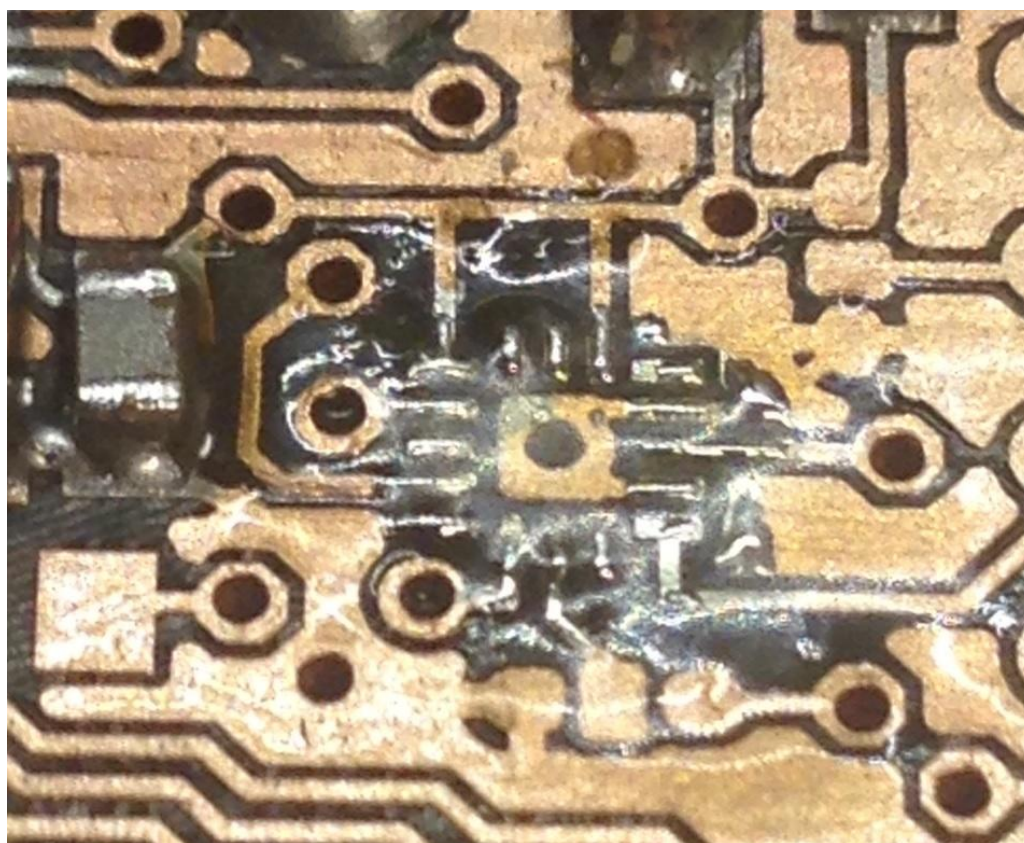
Prototyp akcelerometru MMA8451Q na univerzální DPS
